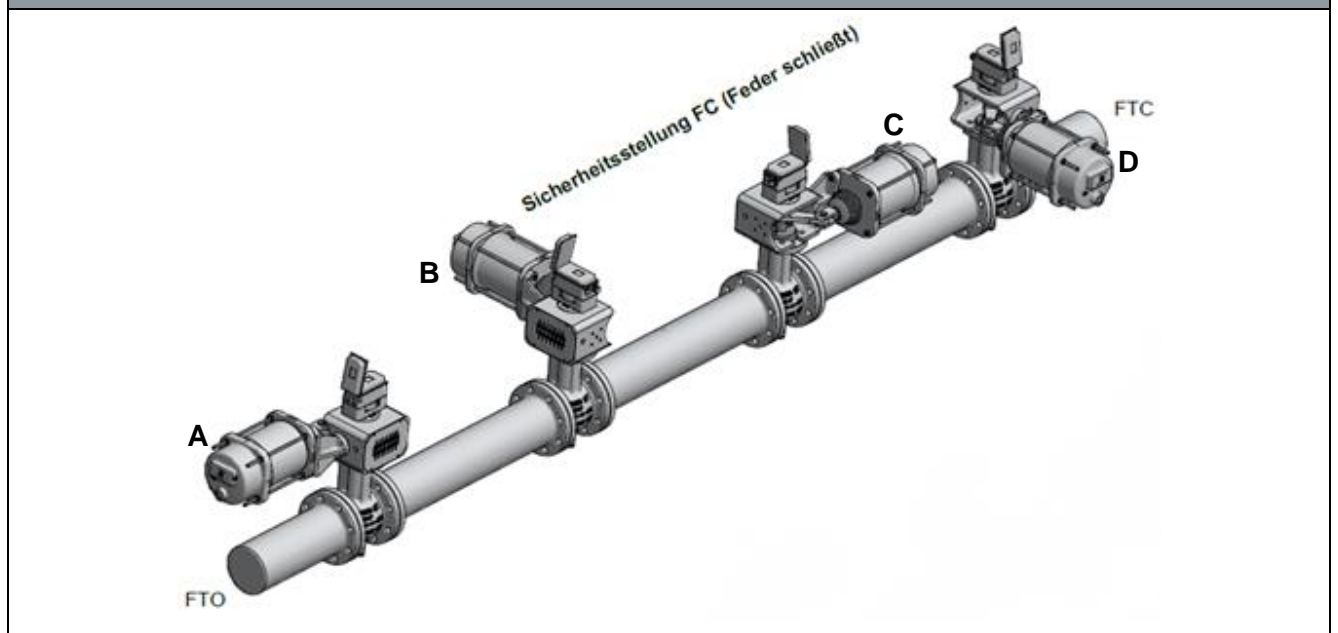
Anbauarten des Antriebs und Einbaulagen des Stellventils
